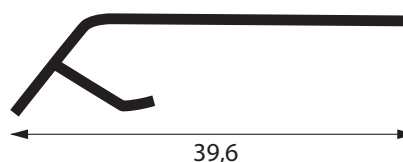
PROTECT ALU sur PLINTHE XL148
